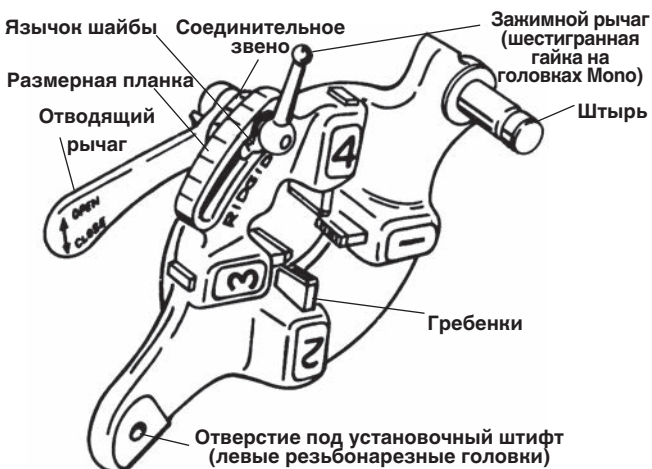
Быстрооткрывающаяся резьбонарезная головка
